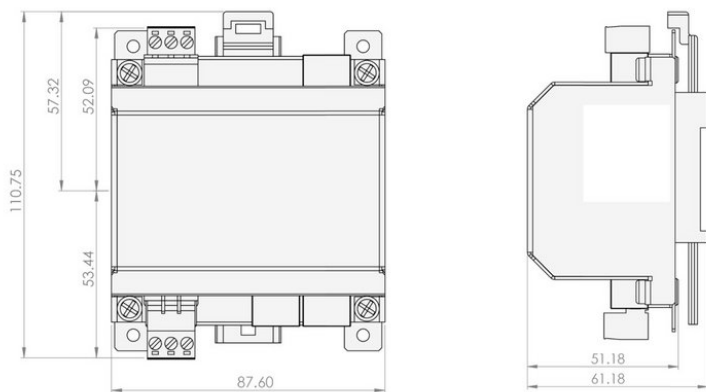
QCBA (med DIN-skene) fysiska dimensioner.
